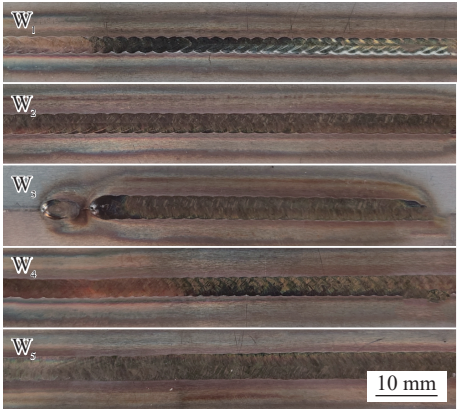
不同焊接工艺参数下焊缝宏观形貌
